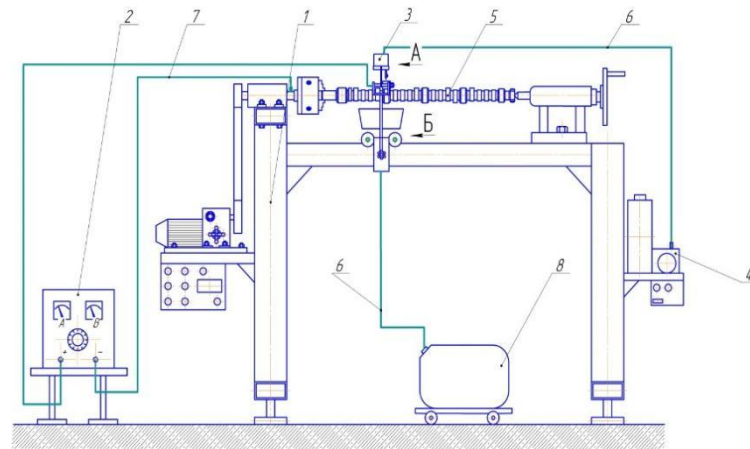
Установка для відновлення опорних шийок розподільних валів: 1 – обертач; 3 – пристосування для контактної хромування; 2 – випрямляч ВСА–5; 4 – пристрій для контролю рівня електроліту; 5 – розподільний вал; 7 – з'єднувальні дроти; 6 – шланги з'єднувальні; 8 – ємність для збору електроліту
